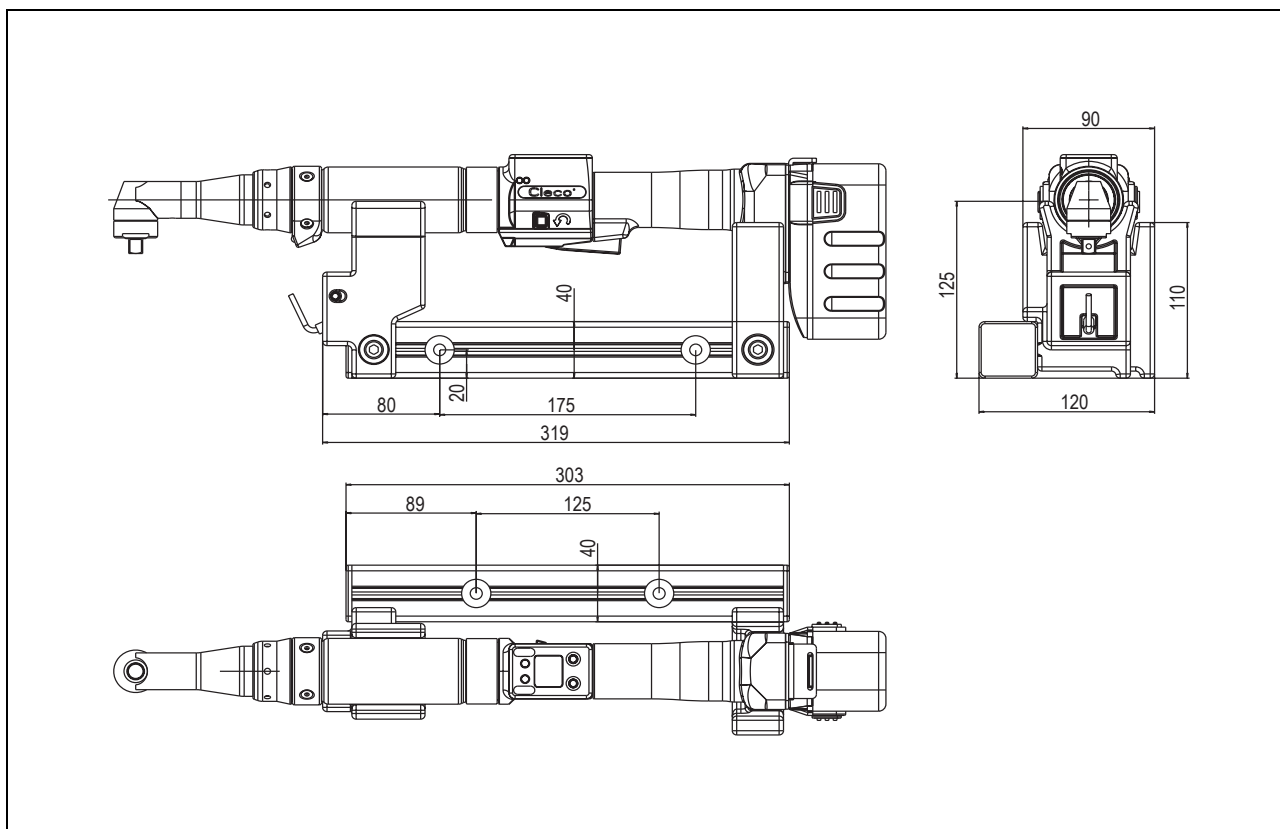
Abmessungen Werkzeughalter (mm)
